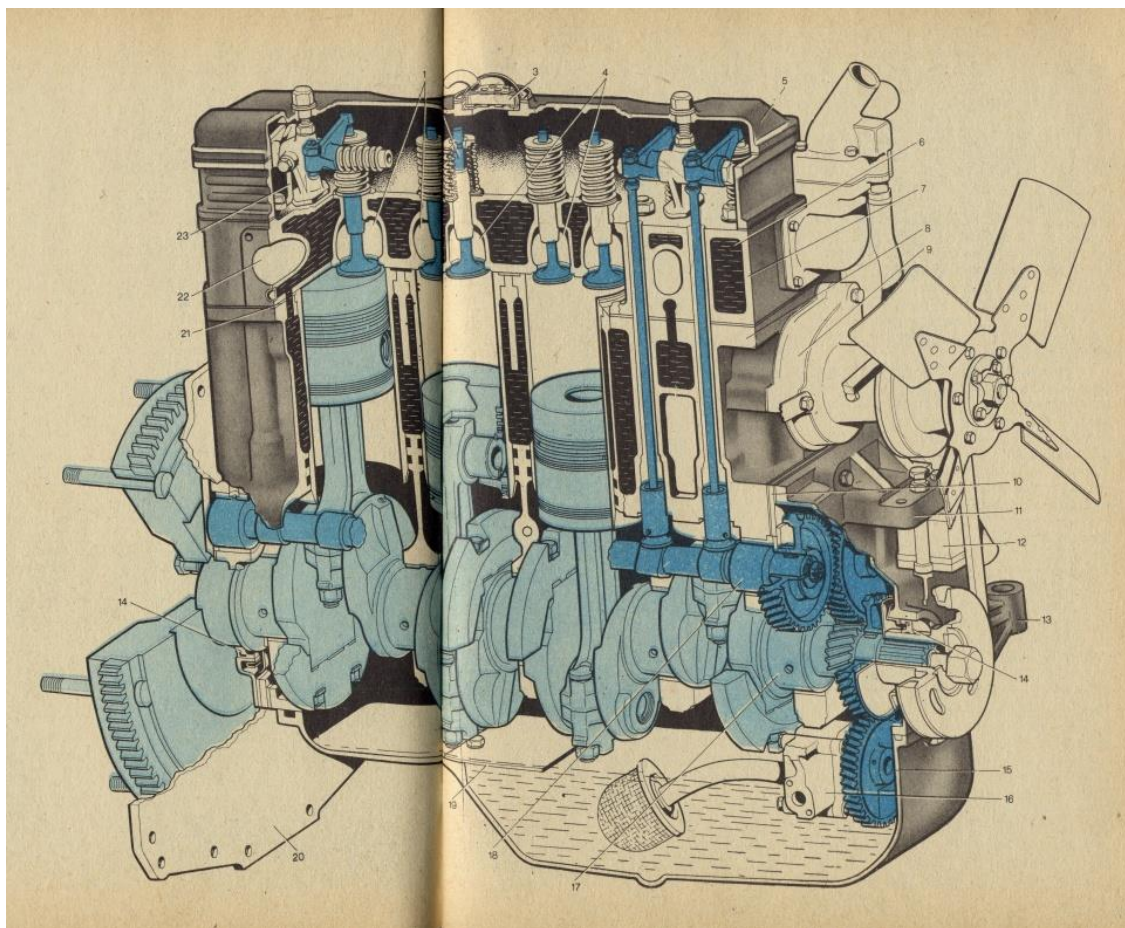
Устройство дизельного двигателя Д - 240: 1 - впускные клапаны третьего и четвертого цилиндров, 2 - клапан, 3 - сапун, 4 - выпускные клапаны второго и третьего цилиндров, 5 - колпак, 6 - водяная рубашка, 7 - головка блока цилиндров, 8 - блок - картер, 9 - водяной насос, 10 - щит распределительных шестерен, 11 - передняя опора двигателя, 12 - амортизатор, 13 - кронштейн передней опоры двигателя, 14 - манжета уплотнительная коленчатого вала, 15 - поддон картера, 16 - масляный насос, 17 - коленчатый вал, 18 - распределительный вал, 19 - успокоитель масла, 20 - задний лист, 21 - металлоасбестовая прокладка, 22 - выпускной канал четвертого цилиндра, 23 - трубка подвода масла к клапанному механизму
